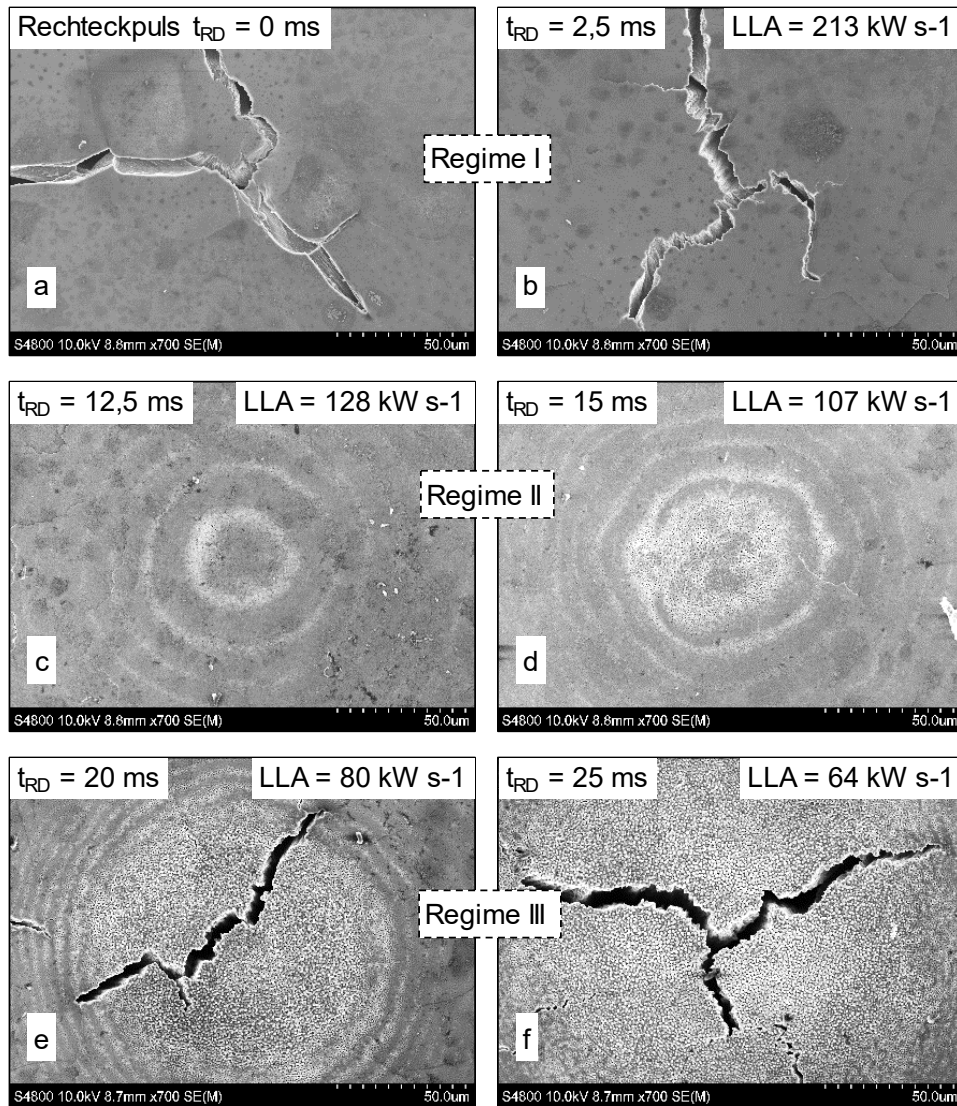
REM-Aufnahmen von Schweißpunktmitten
